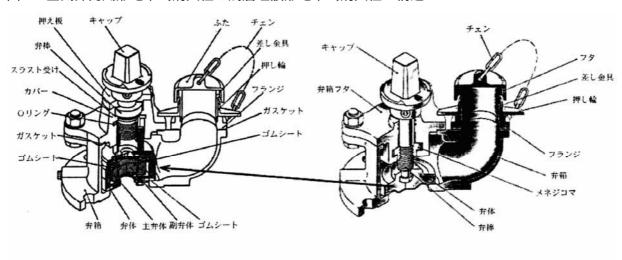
空気弁内蔵形地下式消火栓と浅層埋設形地下式消火栓の構造 Fig. 2 Structure of Air Valve Built-in type Underground Fire Hydrant and Underground Fire Hydrant
